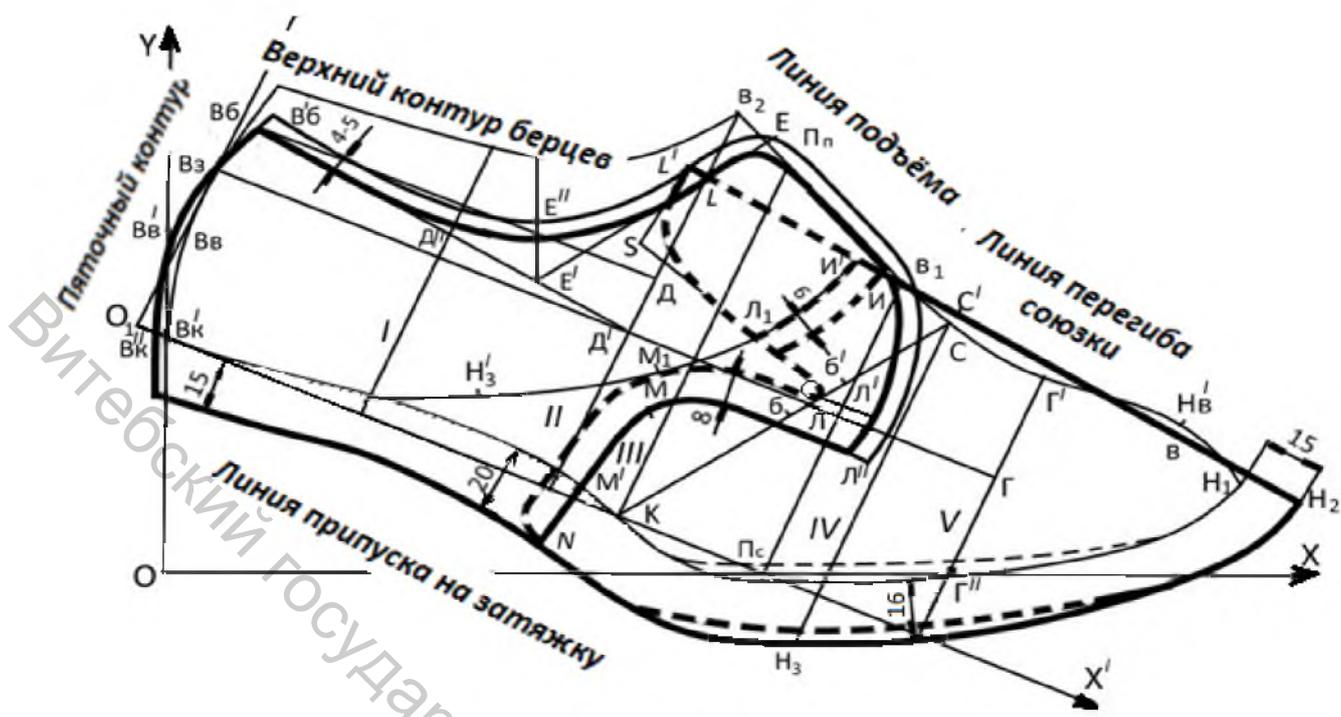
Построение конструктивной основы верха полуботинок с настрочными берцами
